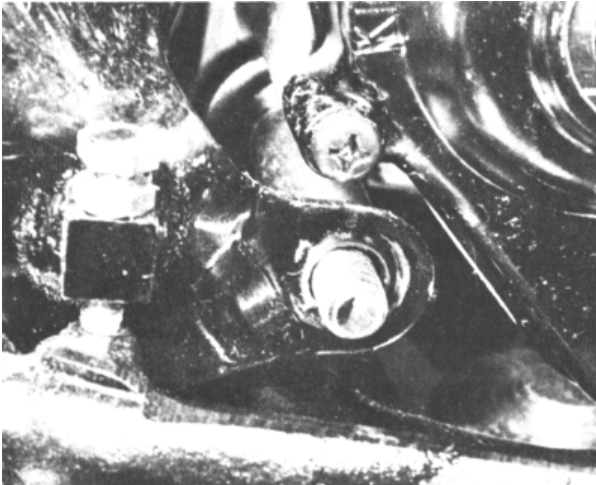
Der untere hintere Motor-Lagerbolzen wird durch Aufhängeösen geführt
